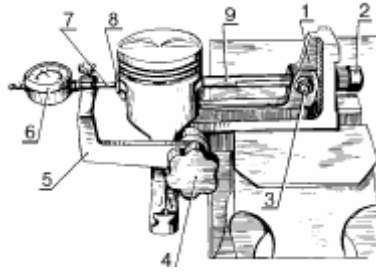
Схема перевірки запресування пальця в шатун.
